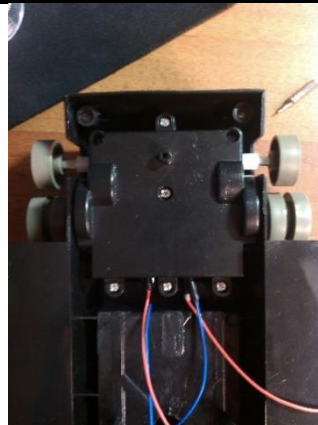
Модуль с редуктором и моторами, установленный в корпус
